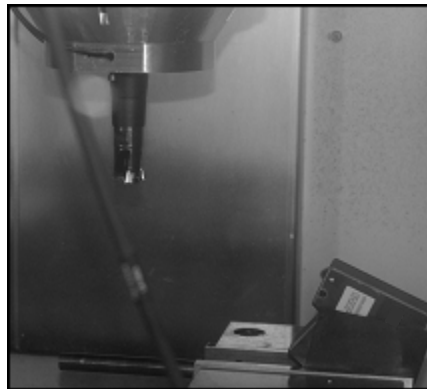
Système d'inspection des outils hors-usinage.
